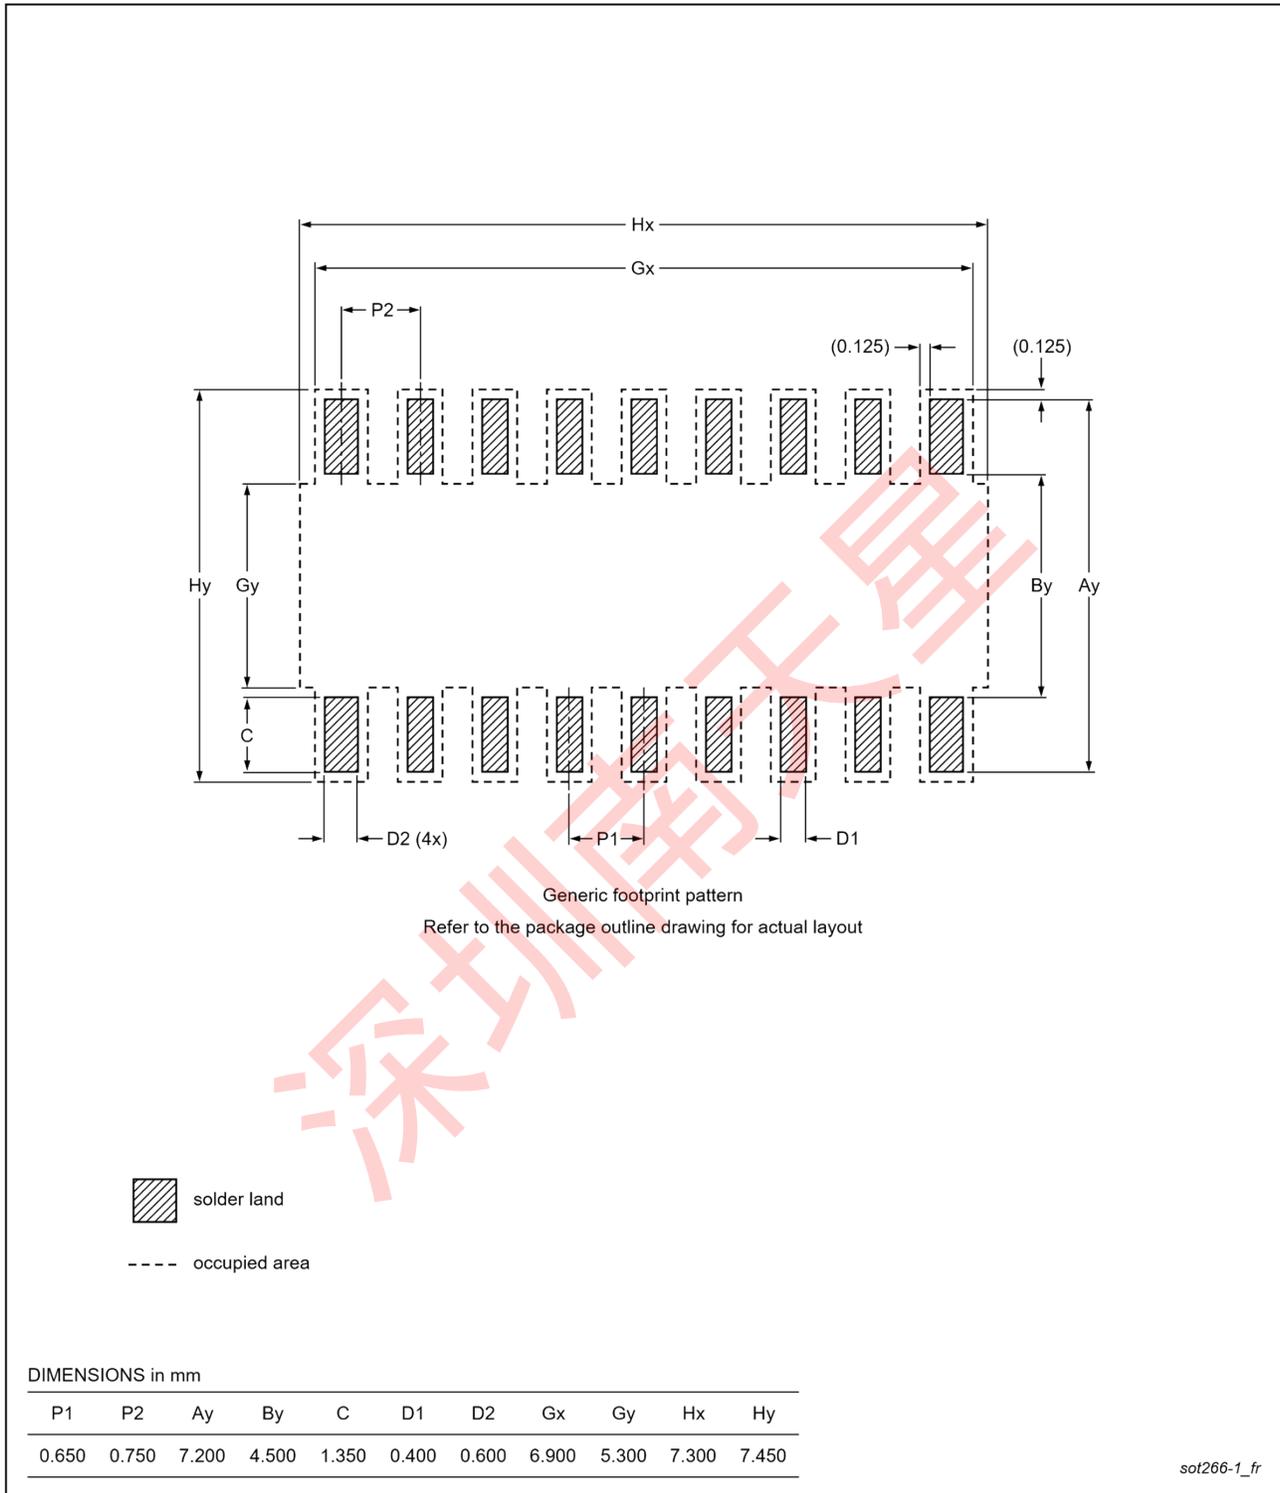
SOT266-1 (SSOP20) 的 PCB 占用空间; 回流 soldering
